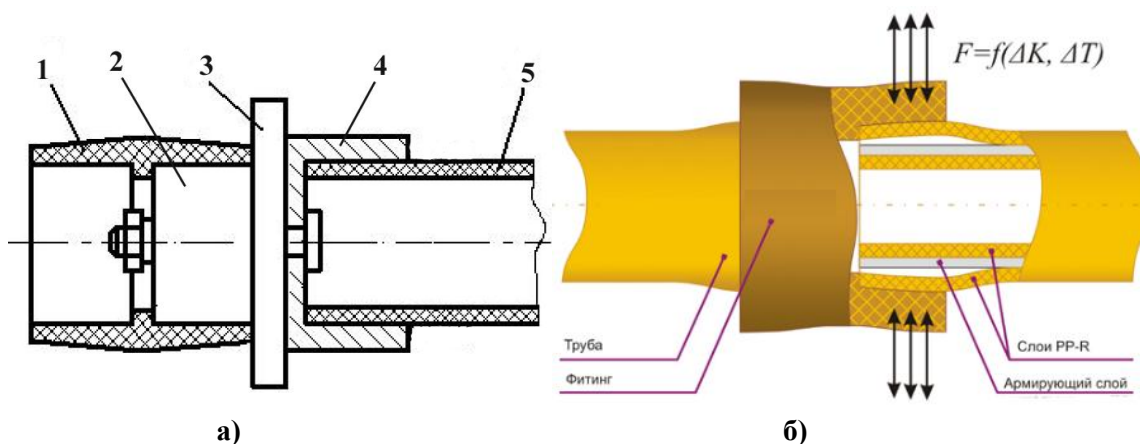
Схеми зварювання композитних труб нагрітим інструментом врозтруб (а) [18] та руйнування розтрубного зварного з'єднання (б) [19]: 1 – муфта; 2 – дорн; 3 – пластина нагрівального інструменту; 4 – гільза; 5 – труба
